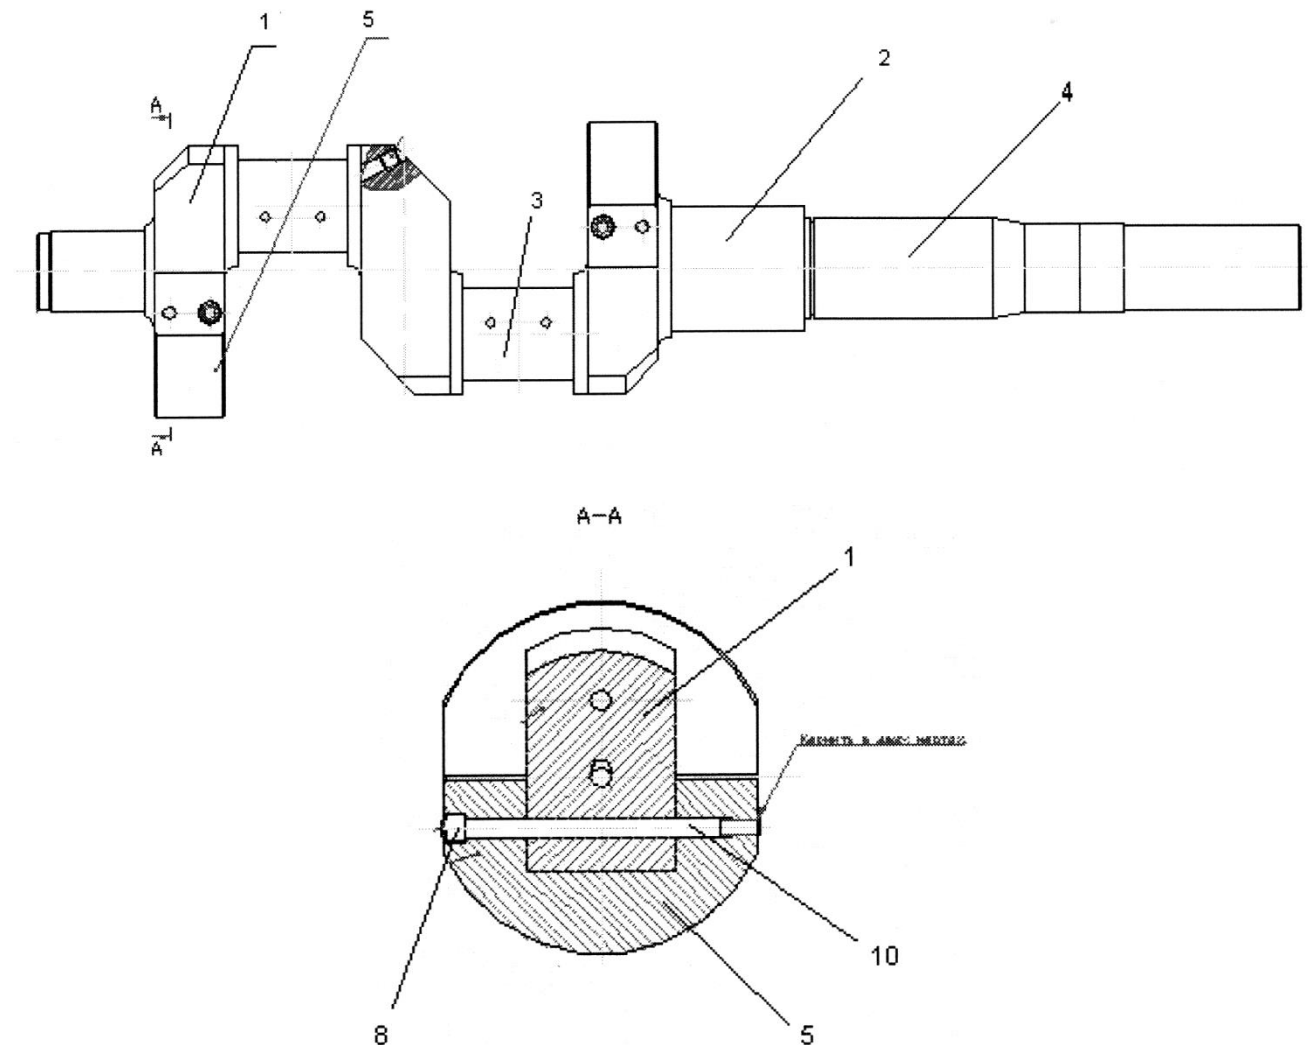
Предлагаемый коленчатый вал компрессора в сборе
